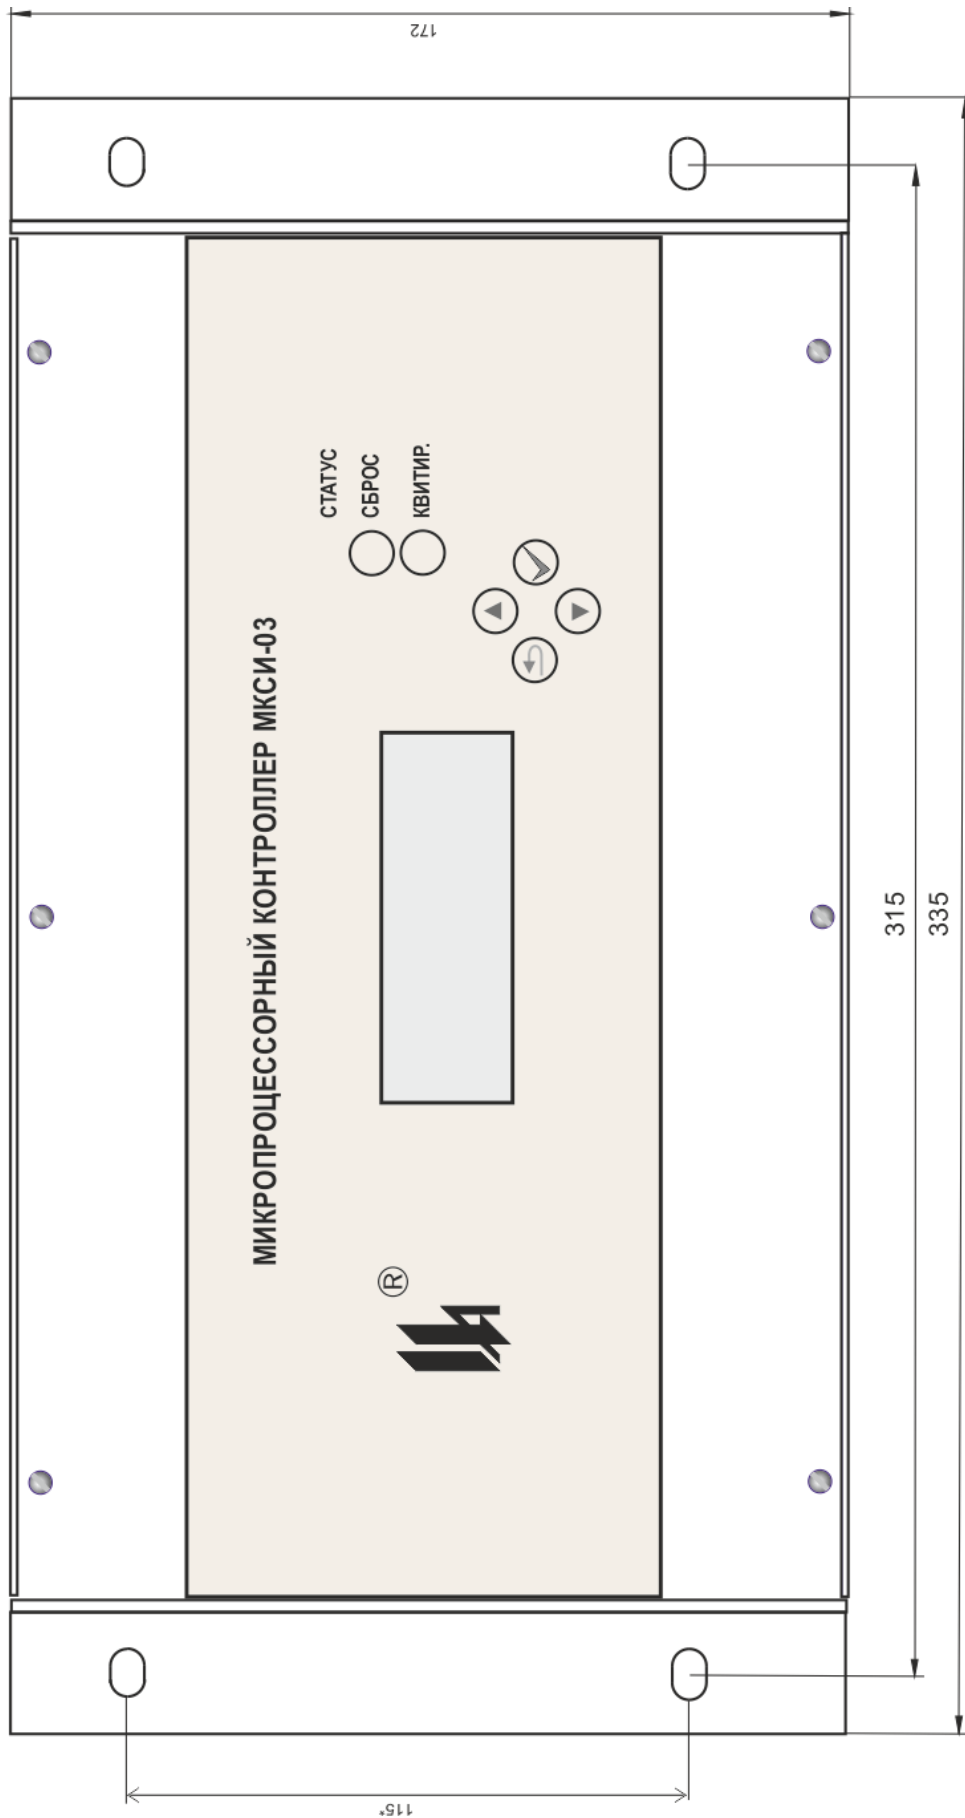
Габаритные и установочные размеры МКСИ-03
